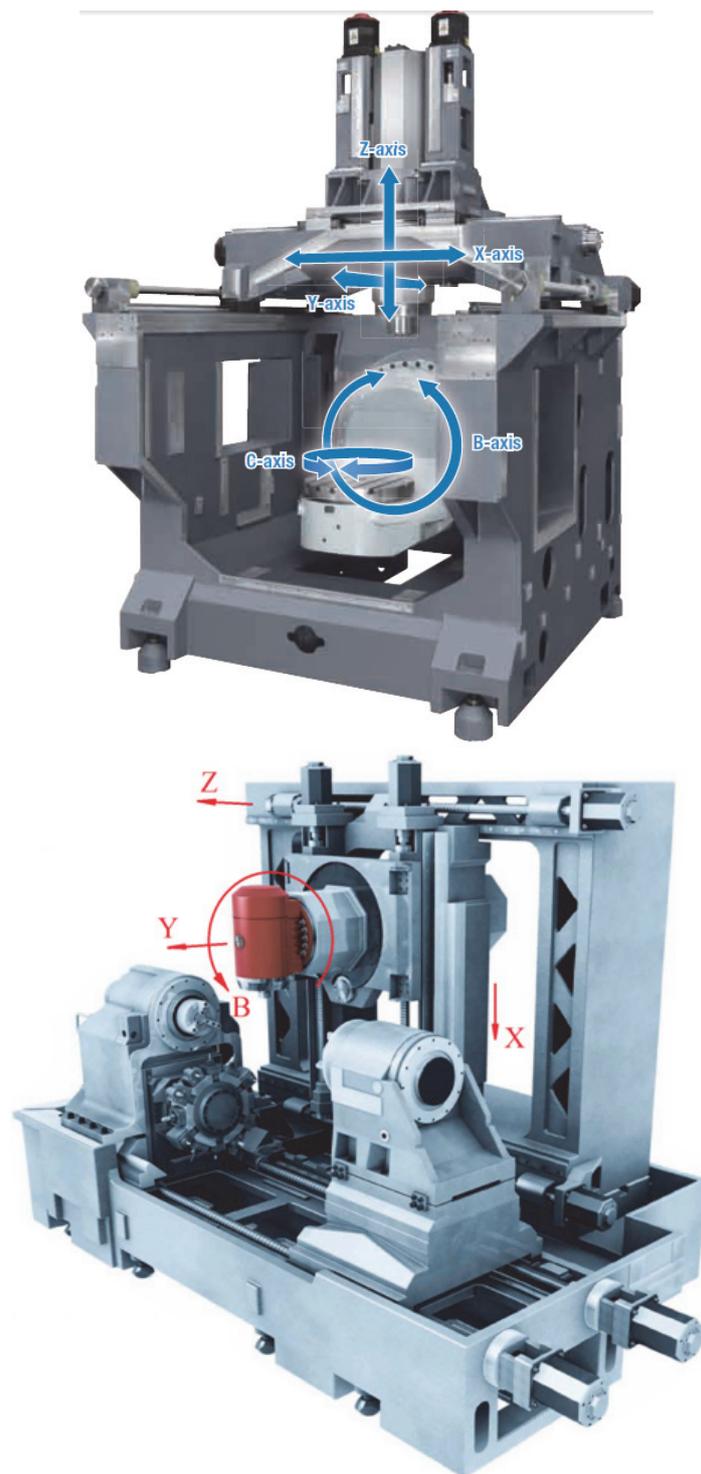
Компоновки фрезерного и токарно-фрезерного станков (для повышения жесткости устройства линейных перемещений типа винт-гайка выполнены парно для каждой оси; справа устройство по оси Y реализовано в виде восьмиугольной жесткой коробки)
